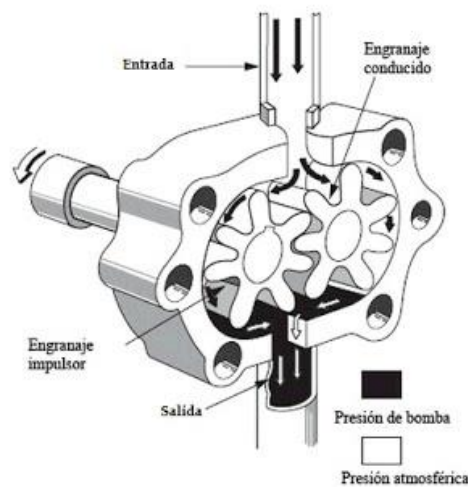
Bomba hidráulica de engranajes externos (*Automatización Industrial- hidráulica*).
